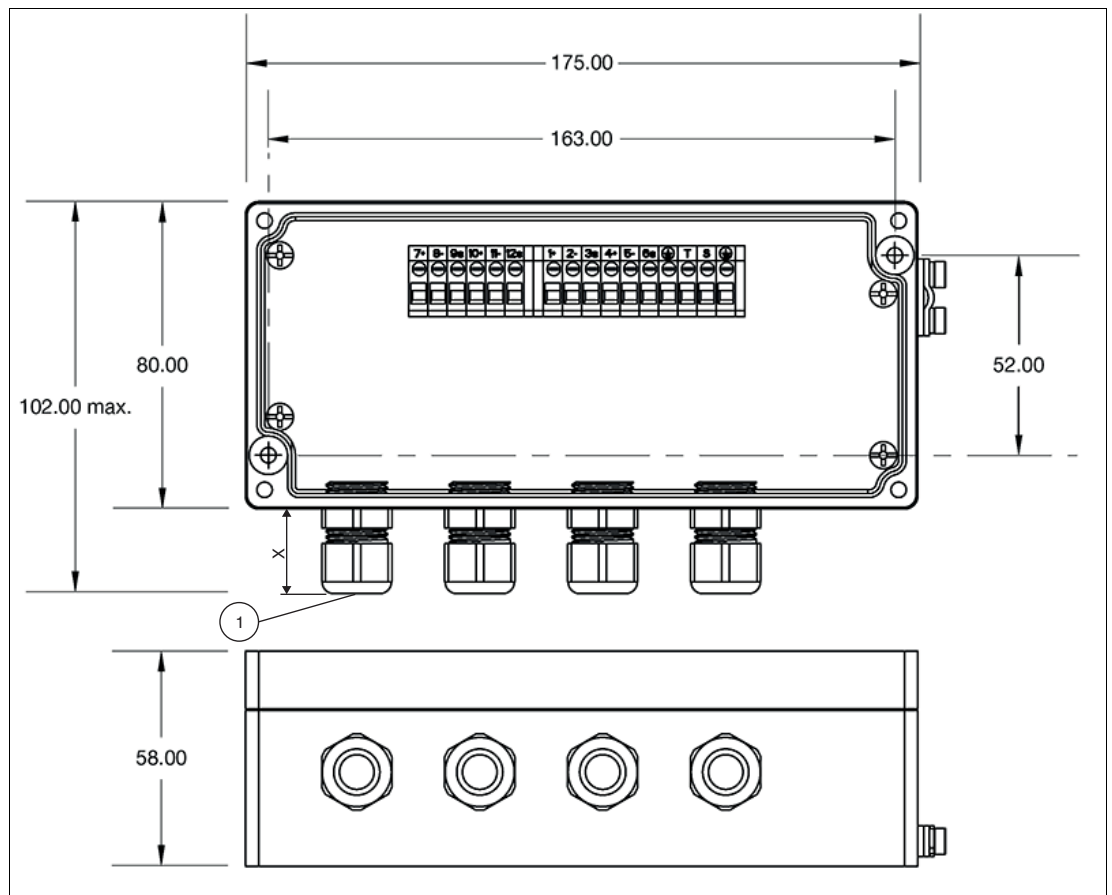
Mechanische Abmessung des F3-Gehäuses
